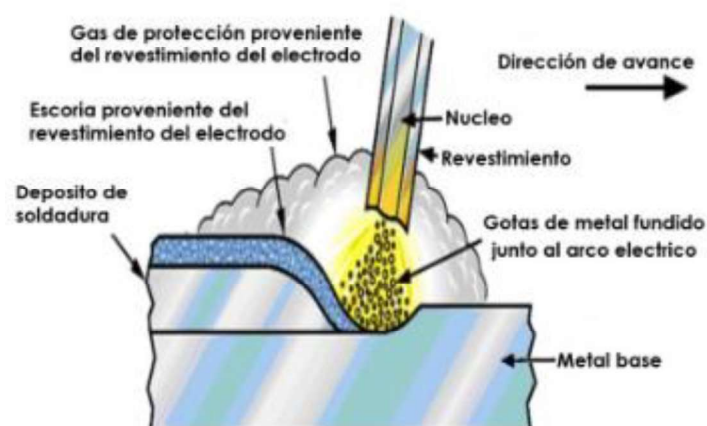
Proceso de soldadura por arco eléctrico (SMAW).
